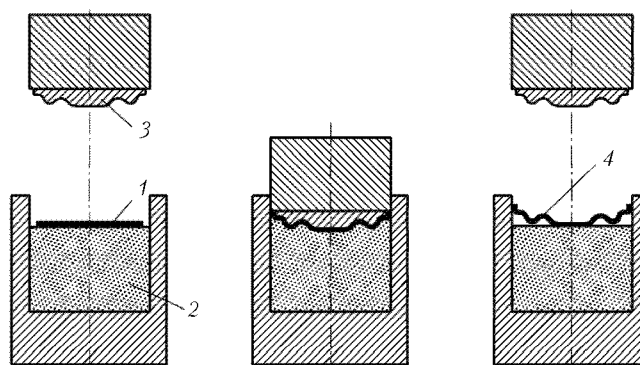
Схема штампования в эластичную форму: 1 — заготовка; 2 — эластичная форма; 3 — матрица; 4 — изделие
